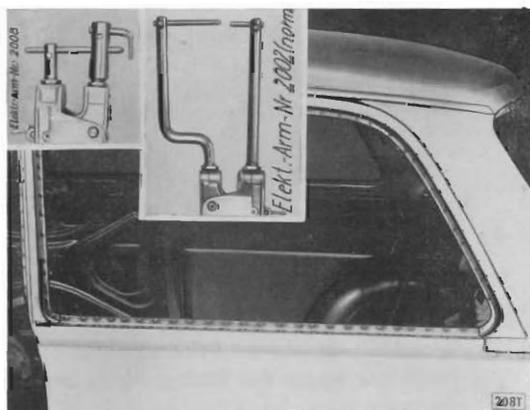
Seitenwand an den unteren Seitenwandfensterrahmen punktgeschweißt
